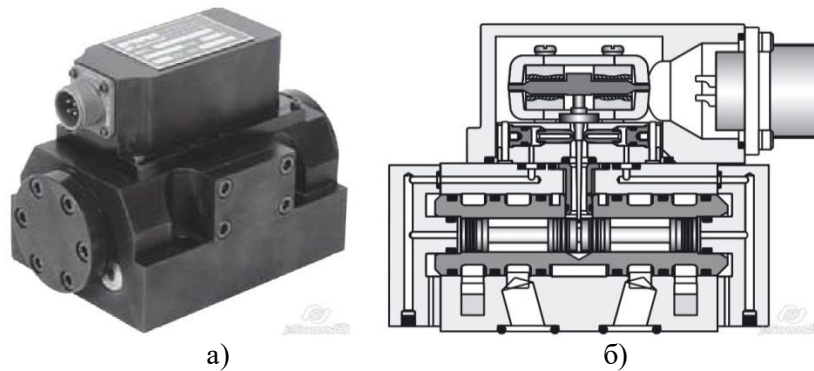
Загальний а) та конструктивний б) вигляди Parker SE60
